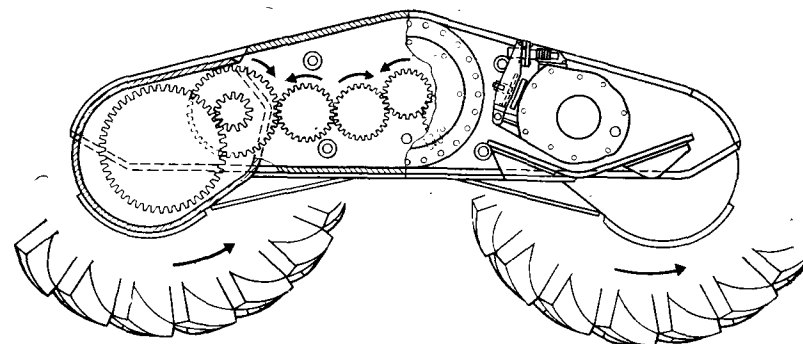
Конструкция ходовой тележки с зубчатой передачей
